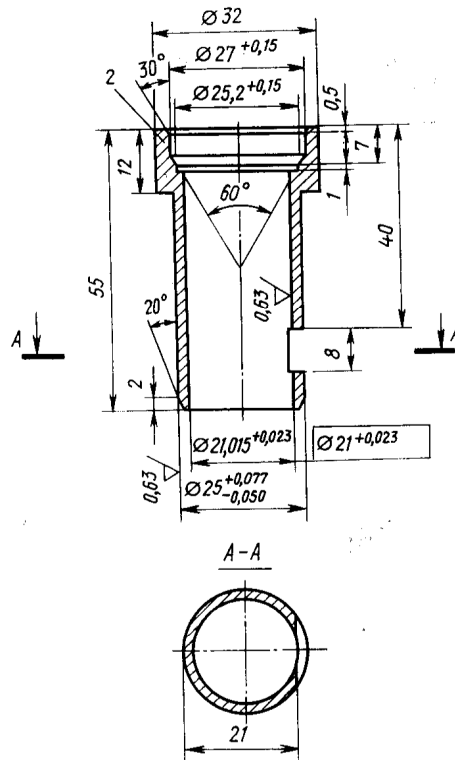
Расточка картера двигателя под ремонтные втулки бонков толкателя:
